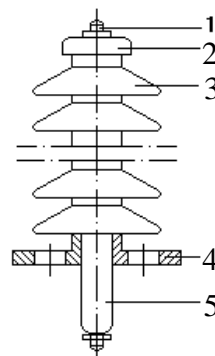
Бакелитовый ввод с полимерной крышкой: 1 – токоведущий стержень; 2- верхний колпачок; 3 – крышка из силиконовой резины (верхняя часть изолятора); 4 - металлический фланец; 5 - выводной терминал.
